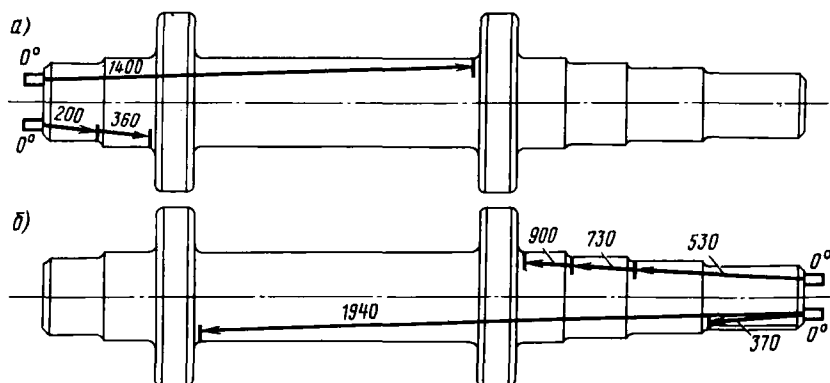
Схемы и зоны контроля прямым искателем со стороны левого (а) и правого (б) торцов главного приводного вала эскалатора ЭМ-4
